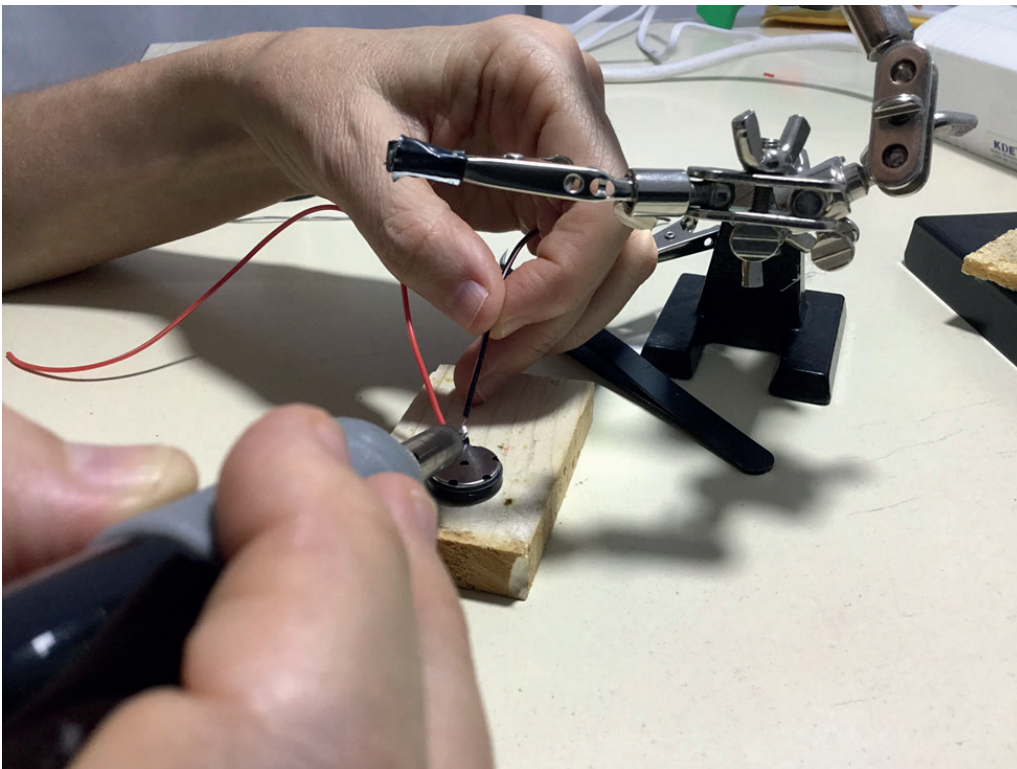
Proceso de soldadura de los cables en los altavoces.
